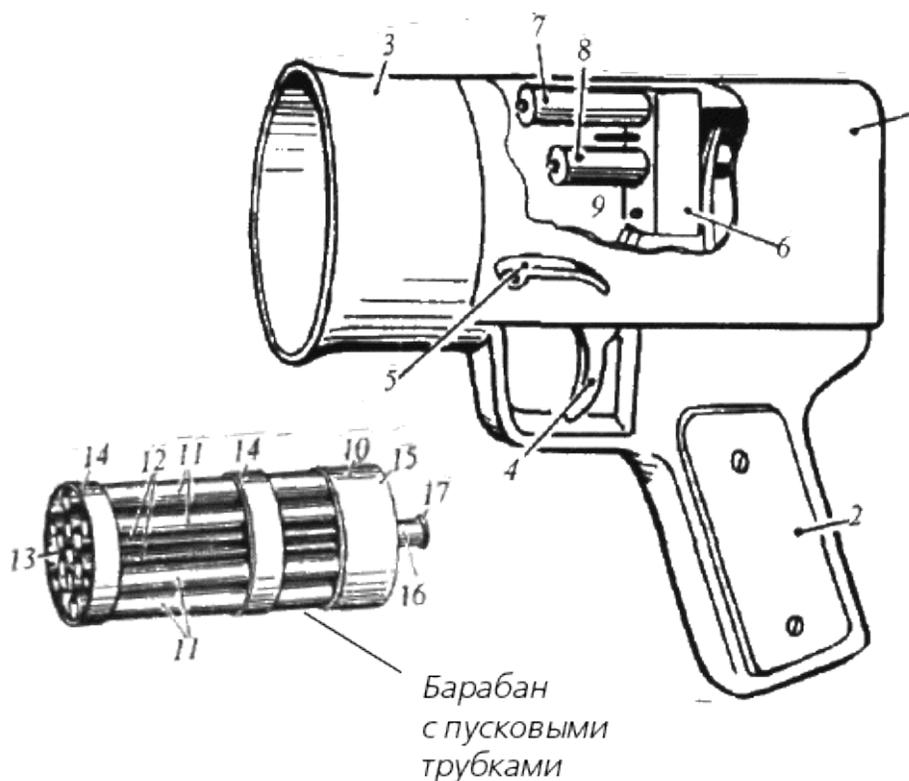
Револьвер для стрельбы реактивными стрелами: 1 – корпус револьвера; 2 – рукоятка; 3 – камера для барабана; 4 – спусковой крючок; 5 – защелка, фиксирующая барабан в рамке; 6 – затвор; 7 – верхний ударник; 8 – средний ударник; 9 – нижний ударник; 10 – барабан; 11 – пусковые
